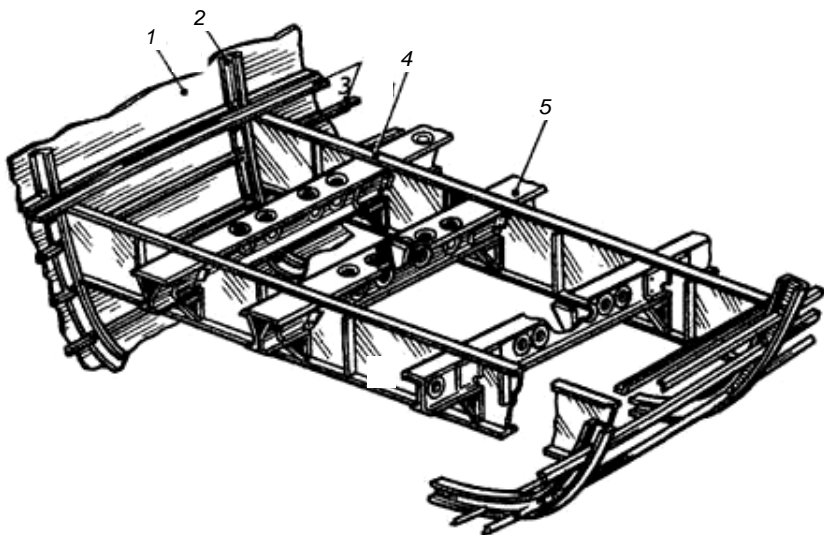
Сборочный узел летательного аппарата из деталей, полученных в разделительных и формообразующих операциях холодной листовой штамповки
